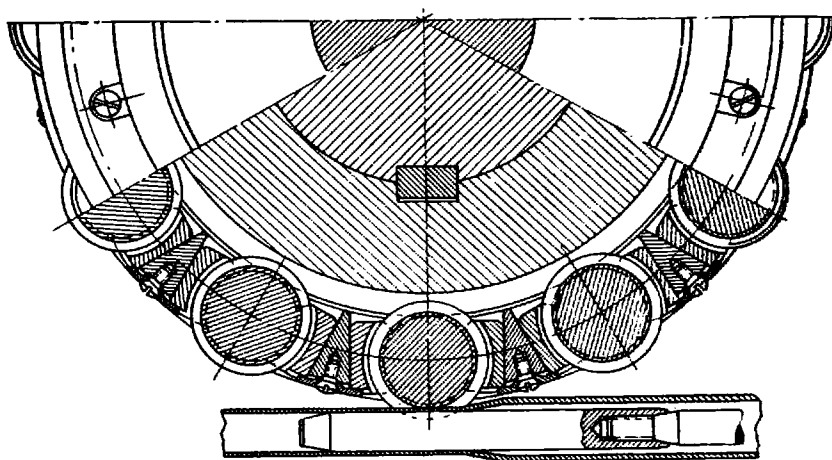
Рабочий инструмент планетарного стана холодной прокатки труб
